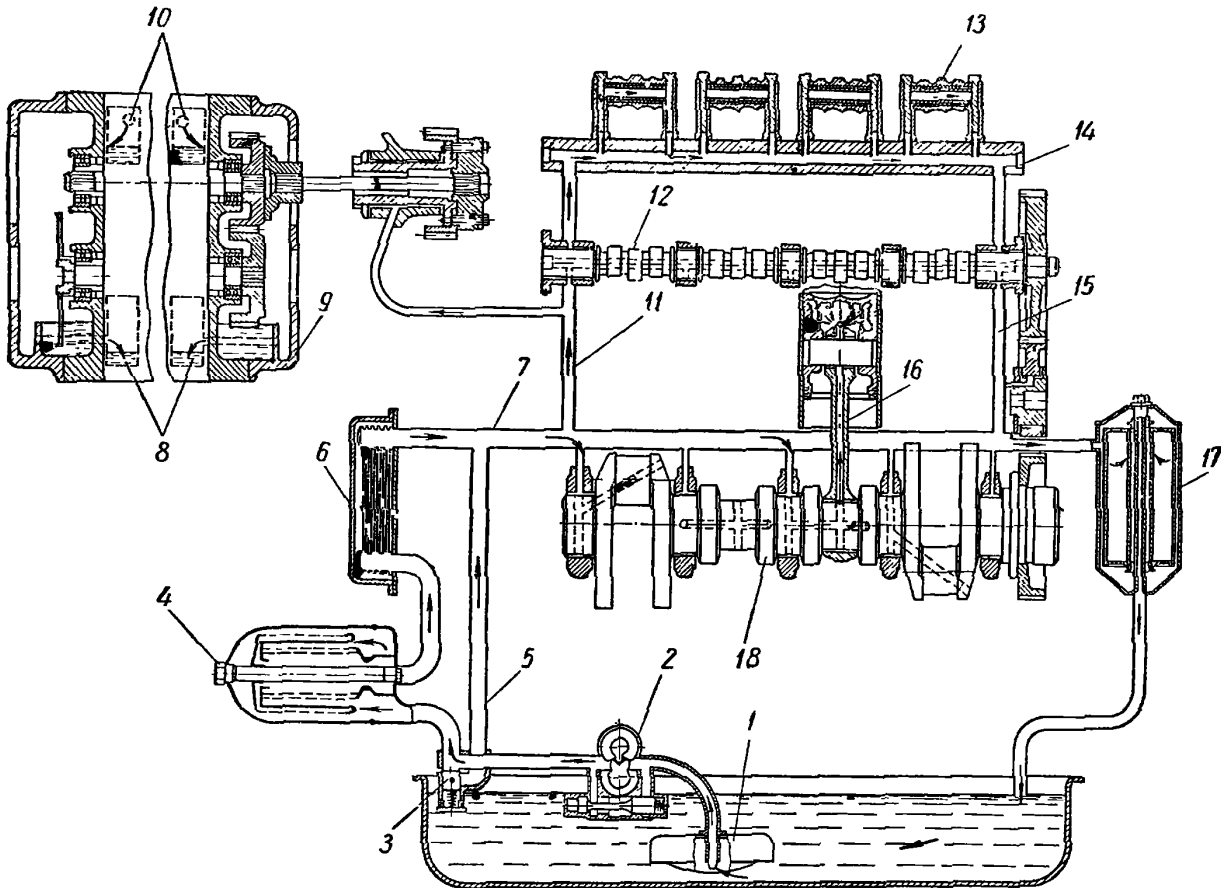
Схема системы смазки карбюраторного двигателя.
